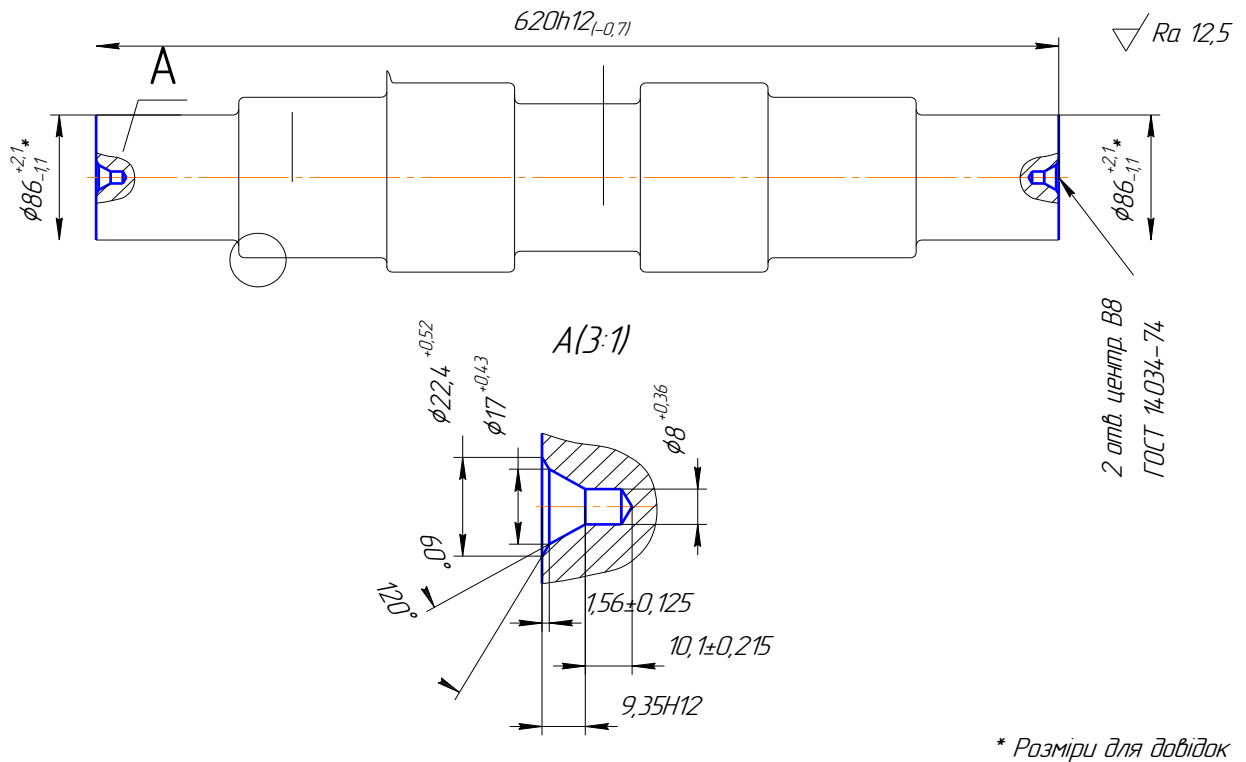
Ескіз фрезерно-центрувальної операції 030
